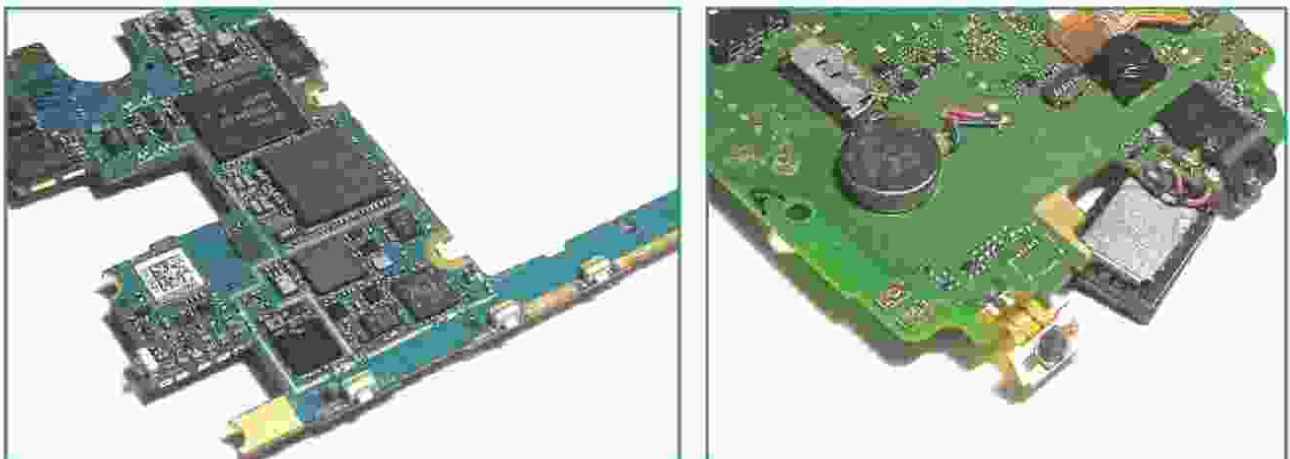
Estos son algunos de los mecanismos de botones que encontrarás. Pueden ser un encapsulado de plástico soldable al PCB o parte de un flex que cierra un circuito.
